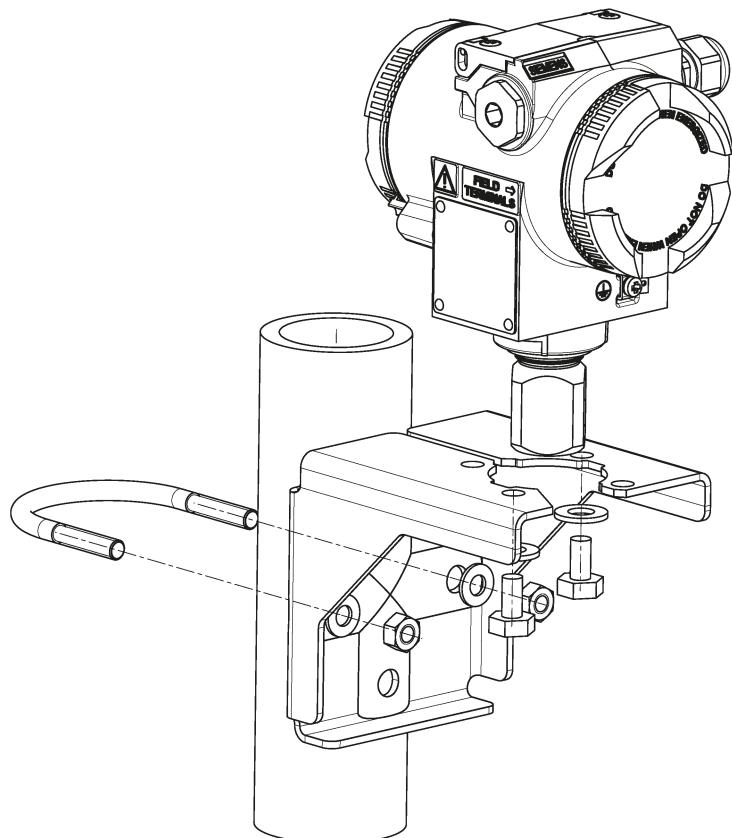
Fissaggio del trasmettitore di pressione con angolare
